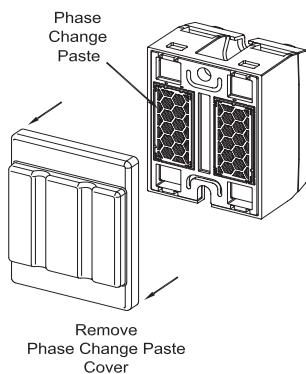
Entfernen Sie die Abdeckung, bevor Sie sie am Gehäuse oder Kühlkörper des Gehäuses befestigen.
